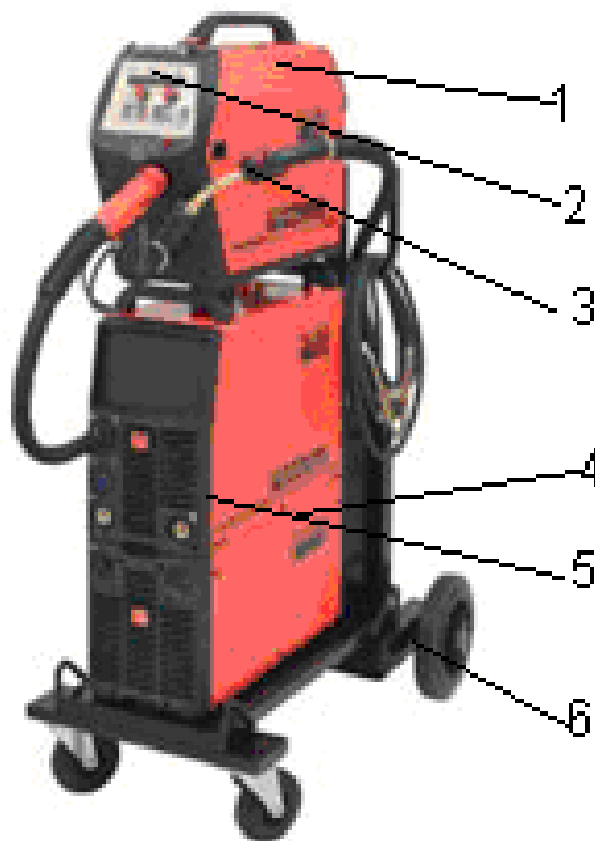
Сварочный аппарат Kemppi FastMig
